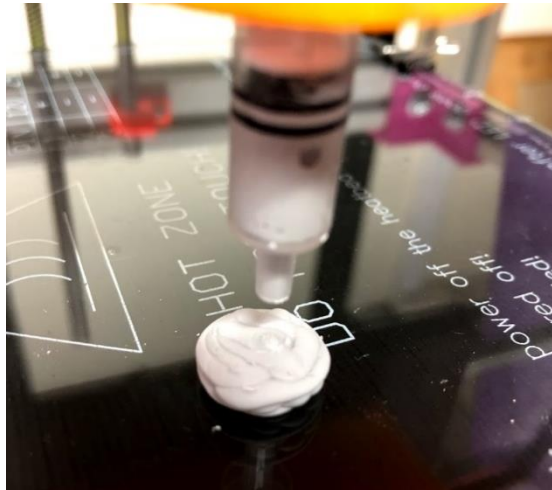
Impresión cilindro con dimensiones aumentadas 1,5 veces.
